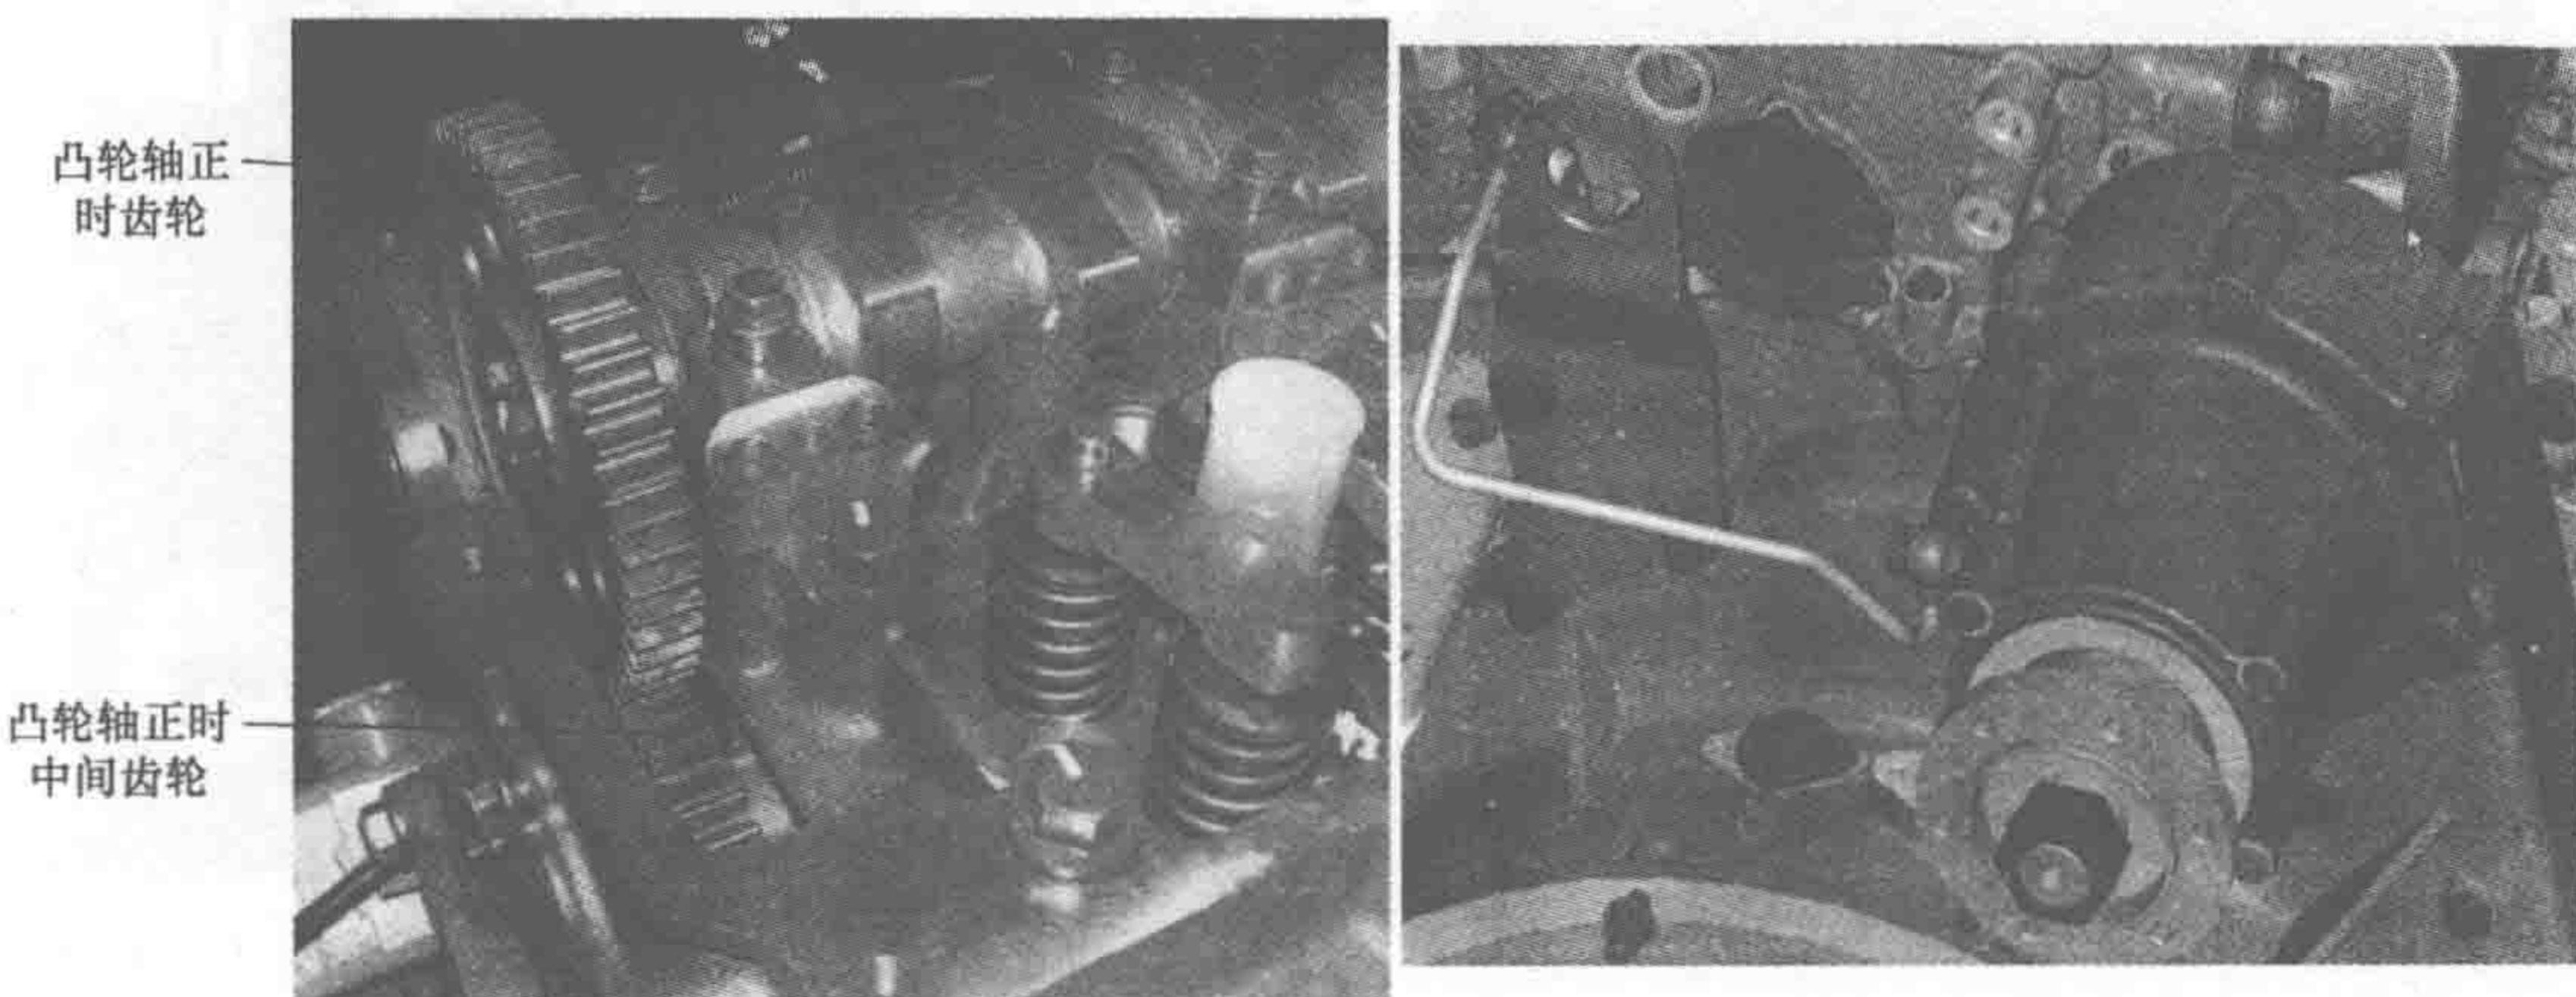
凸轮轴正时齿轮与凸轮轴正时中间齿轮的安装情况
